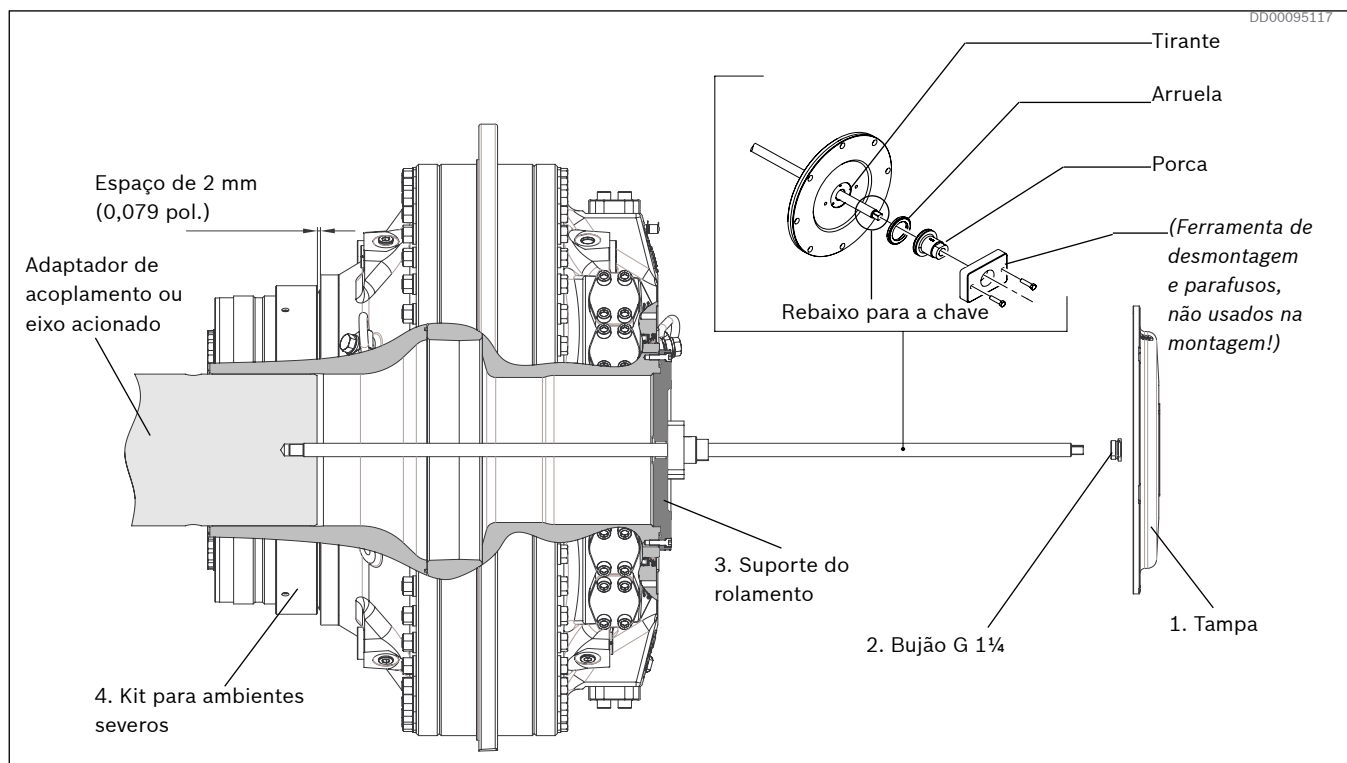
Montagem do motor de acoplamento com a ferramenta de montagem
